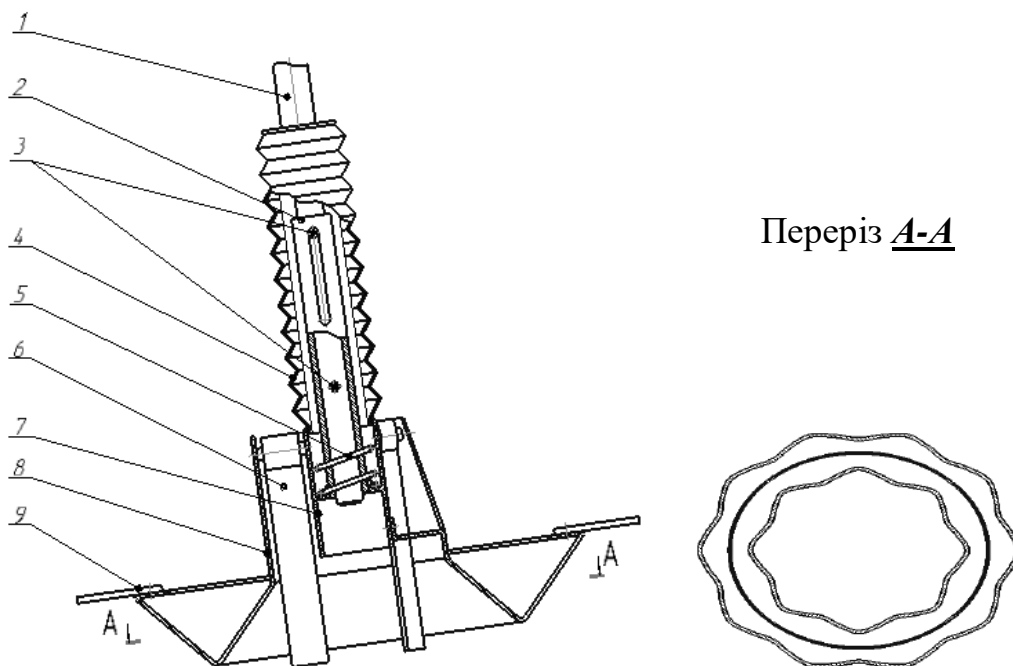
Пристрій для одночасного зрізування гички та очищення головок коренеплодів цукрових буряків [6]: 1 – вал, 2 – втулка, 3 – штифт, 4 – кожух, 5 – пружина, 6 – еластична лопать, 7 – маточина, 8 – диск, 9 – ніж
